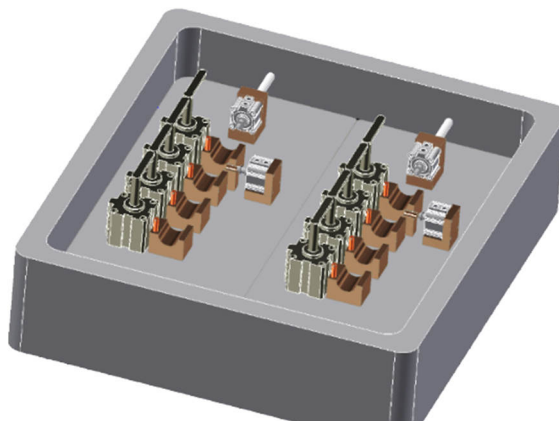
Model geometryczny komór: grzewczej i chłodzącej pieca wodorowego
